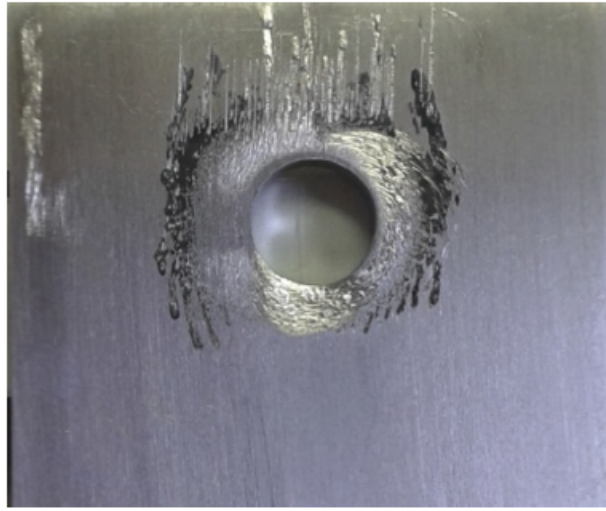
Usure par frottement d'une plaque en aluminium d'un assemblage double recouvrement sollicité en fatigue [Ferjaoui15]
